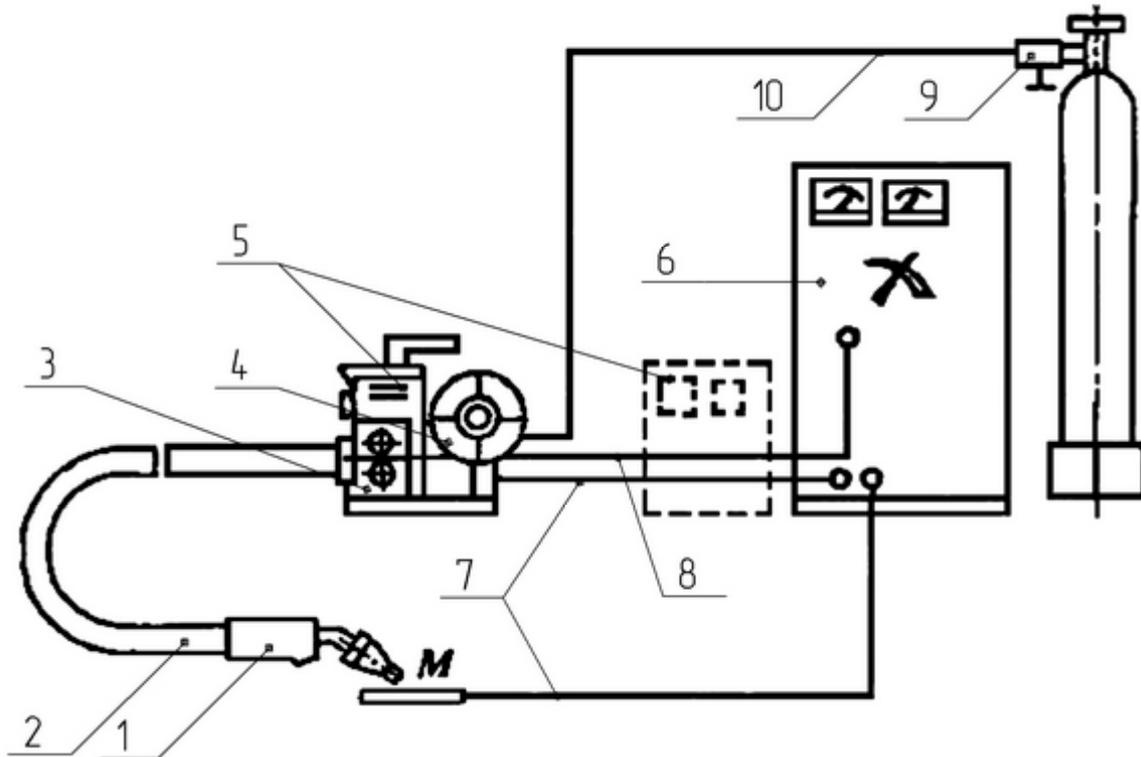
Шланговый полуавтомат для сварки в защитных газах
